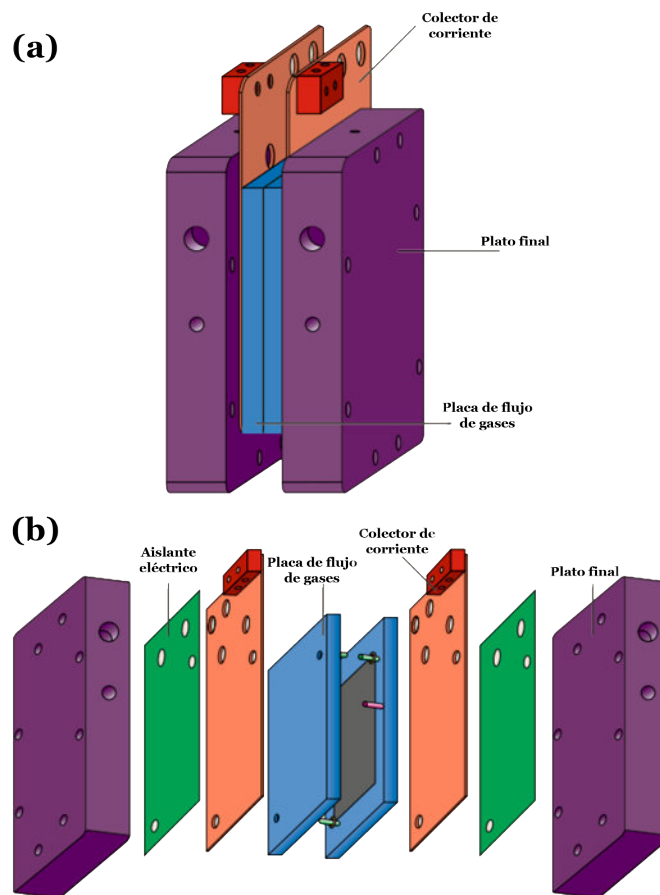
Componentes básicos de una celda de combustible. (a) celda de combustible unitaria, (b) vista explosionada de la celda de combustible unitaria. Adaptado de [44].
